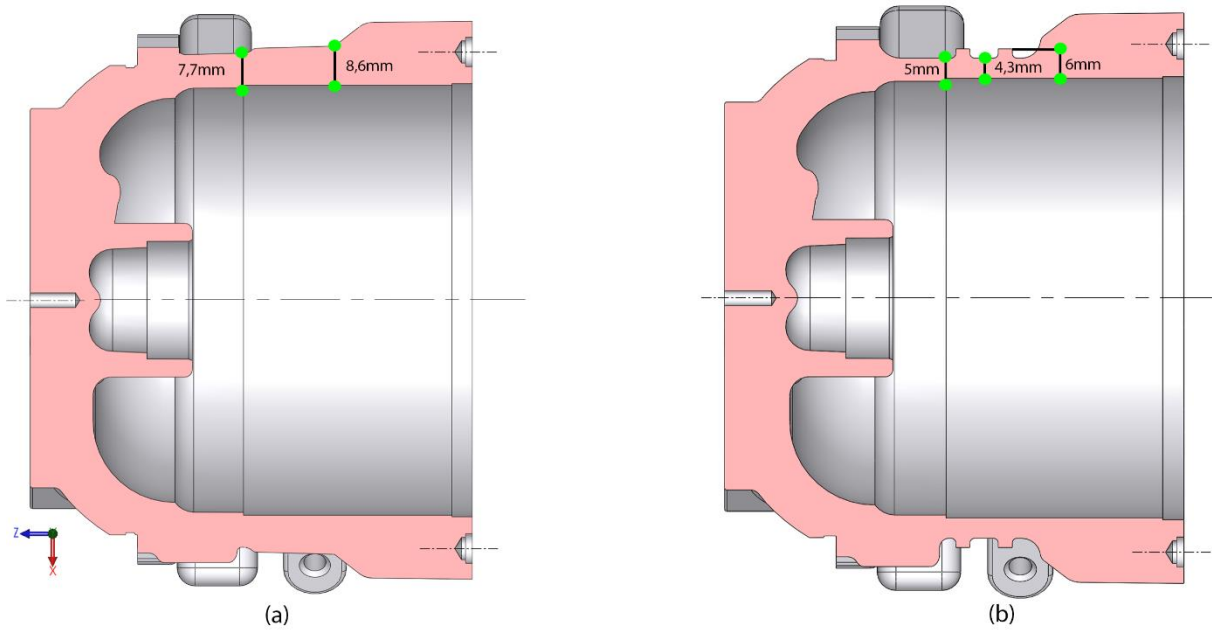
a) Vista em corte da configuração original e b) vista em corte da configuração obtida.
